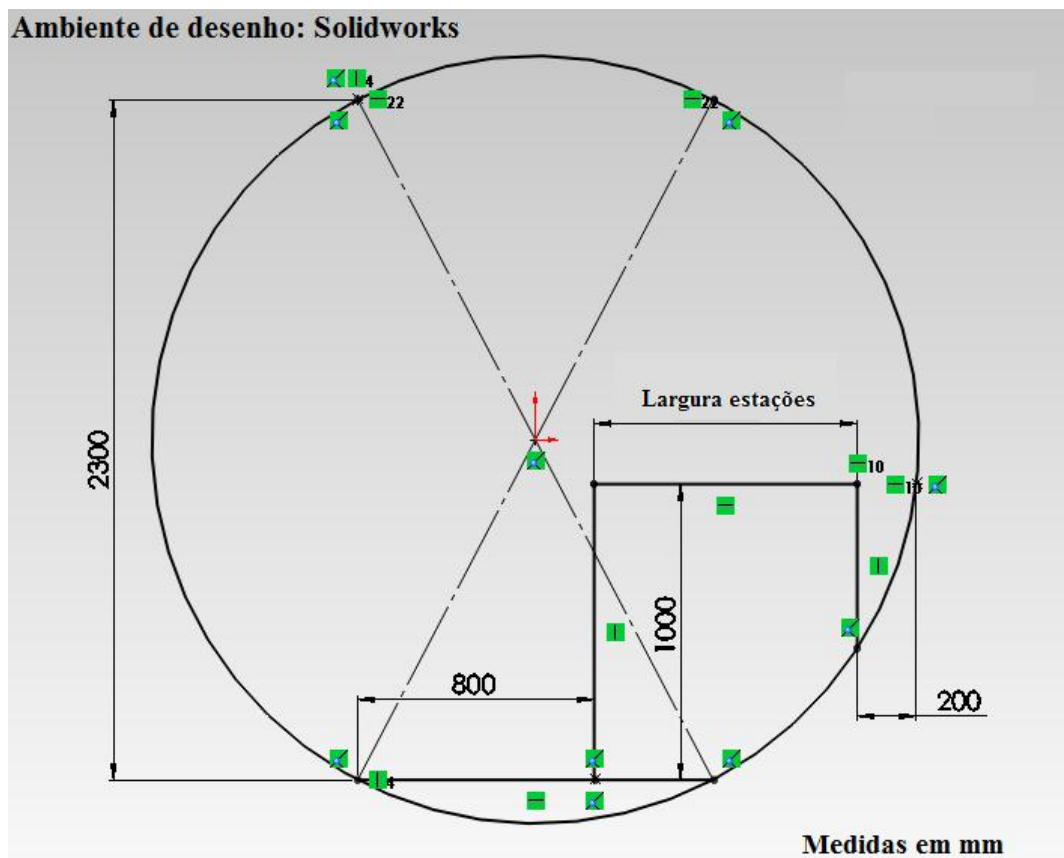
Dimensionamento da secção transversal da estrutura tubular.
